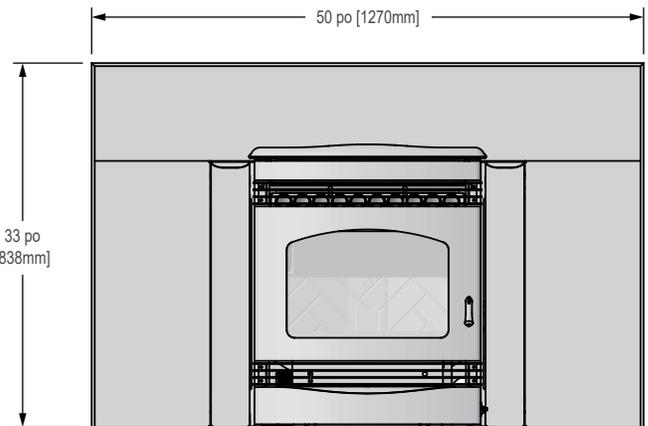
Vue frontale avec un grand ensemble de panneaux de base
